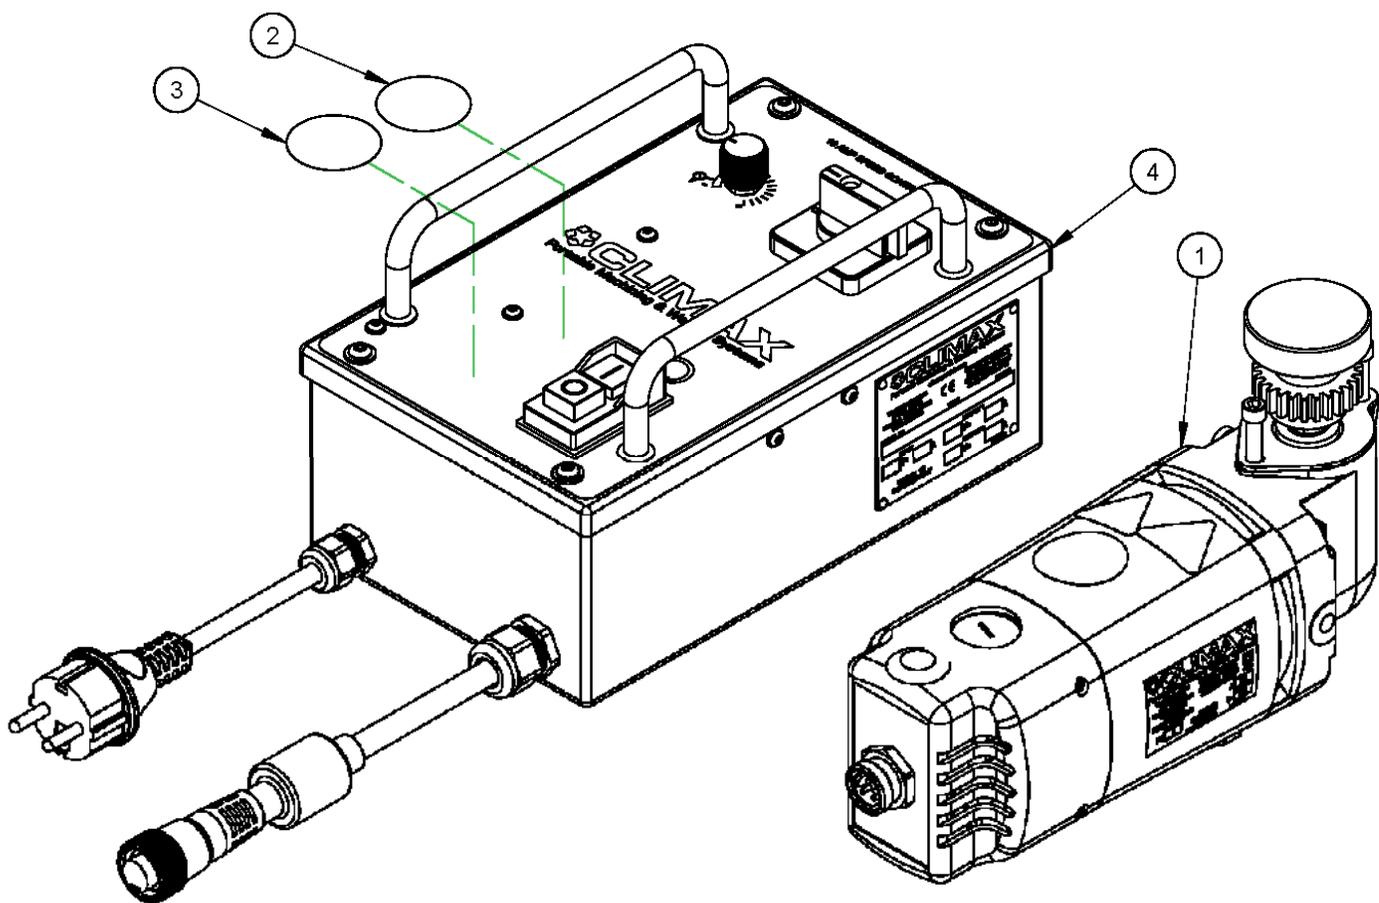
LISTA DE PIEZAS DEL CONJUNTO DEL MOTOR (N/P 11895)
